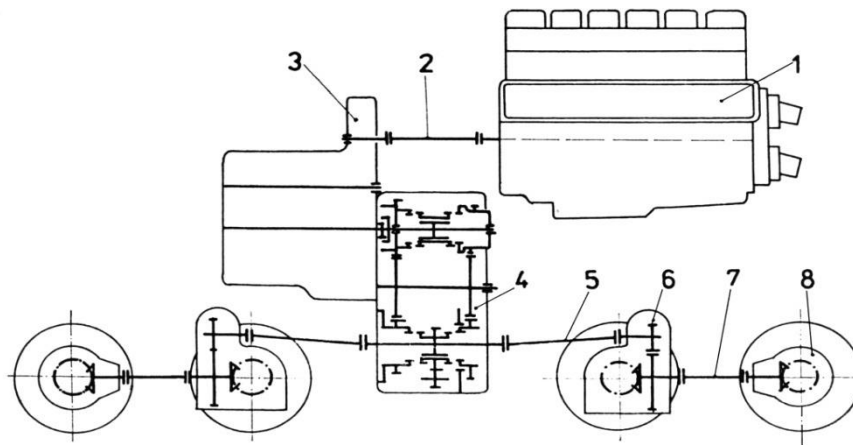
Schema cinematică a transmisiei hidraulice pentru LDH 125: 1- motor diesel 6 LDA 28 B; 2 - x de legătură; 3 - turbo transmisia hidraulică tip TH 2, 4 - reductor inversor tip NG 1200/2; 5 - ax cardanic 367/6 1/2 ; 6 - atac dublu de osie A 35 SK; 7 - ax cardanic 367/7; 8 - atac simplu de osie A 35 [34]
